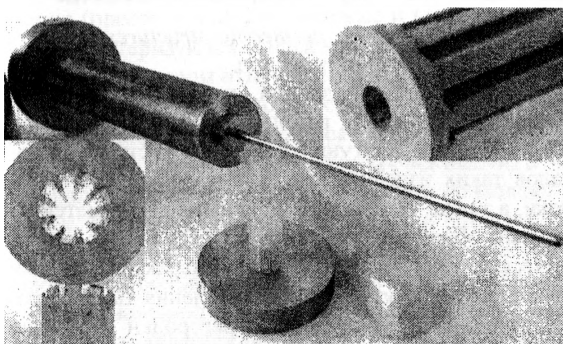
Вид пресс-формы для прессования КПС с паровыми каналами и фрагмент спрессованной заготовки
